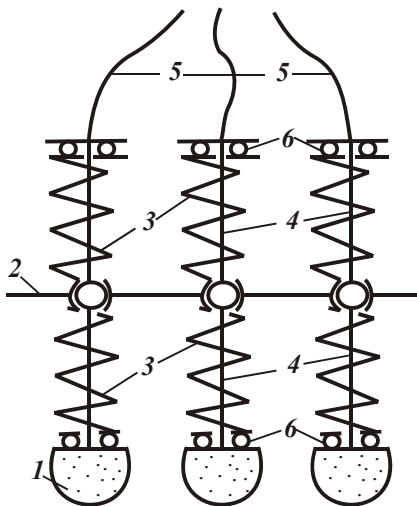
Шлифовальный инструмент для обработки фасонных поверхностей: 1 - шлифовальный шар (сфера); 2 - несущая плита - корпус; 3 - пружины; 4 - жесткий вал с шаровой опорой; 5 - гибкий вал, соединенный с жестким валом для вращения шара; 6 - подшипники.
